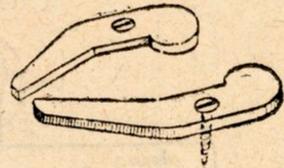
Mâchoires-arrêt pour bouts de planches.
